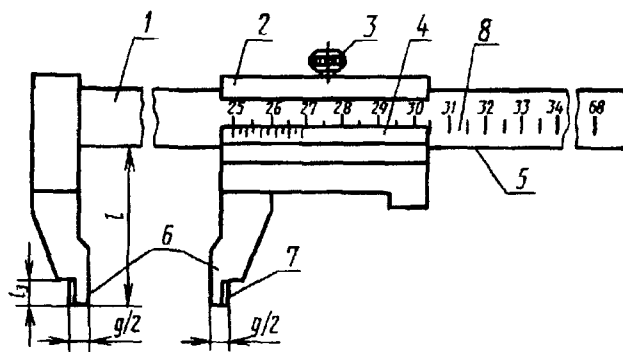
1- штанга; 2- рамка; 3 зажимаючий елемент; 4- ноніус; 5- робоча поверхня штанги; 6- губки з плоскими вимірювальними поверхнями для вимірювання зовнішніх розмірів; 7- губки з циліндричними вимірювальними поверхнями для вимірювання внутрішніх розмірів; 8- шкала штанги
